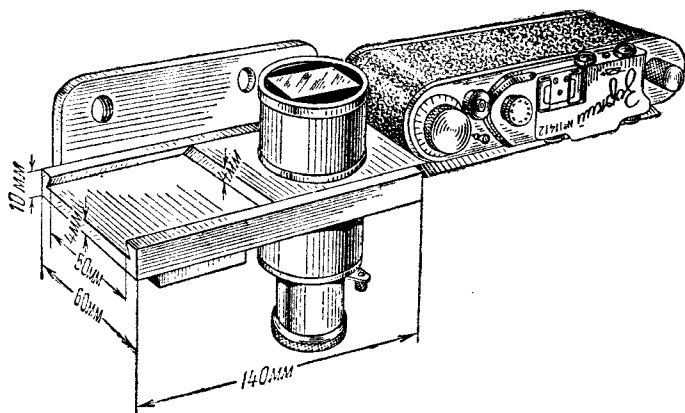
Устройство для наводки по матовому стеклу с передвижной планкой
